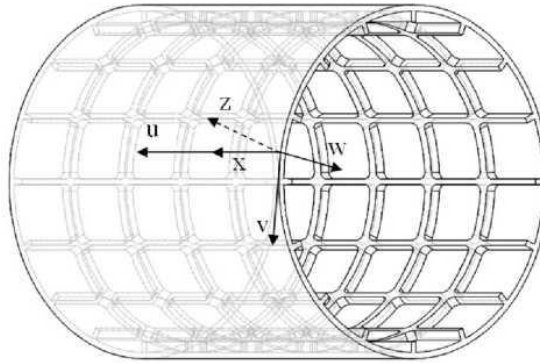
Ескіз несучої циліндричної оболонки бака ракети-носія
